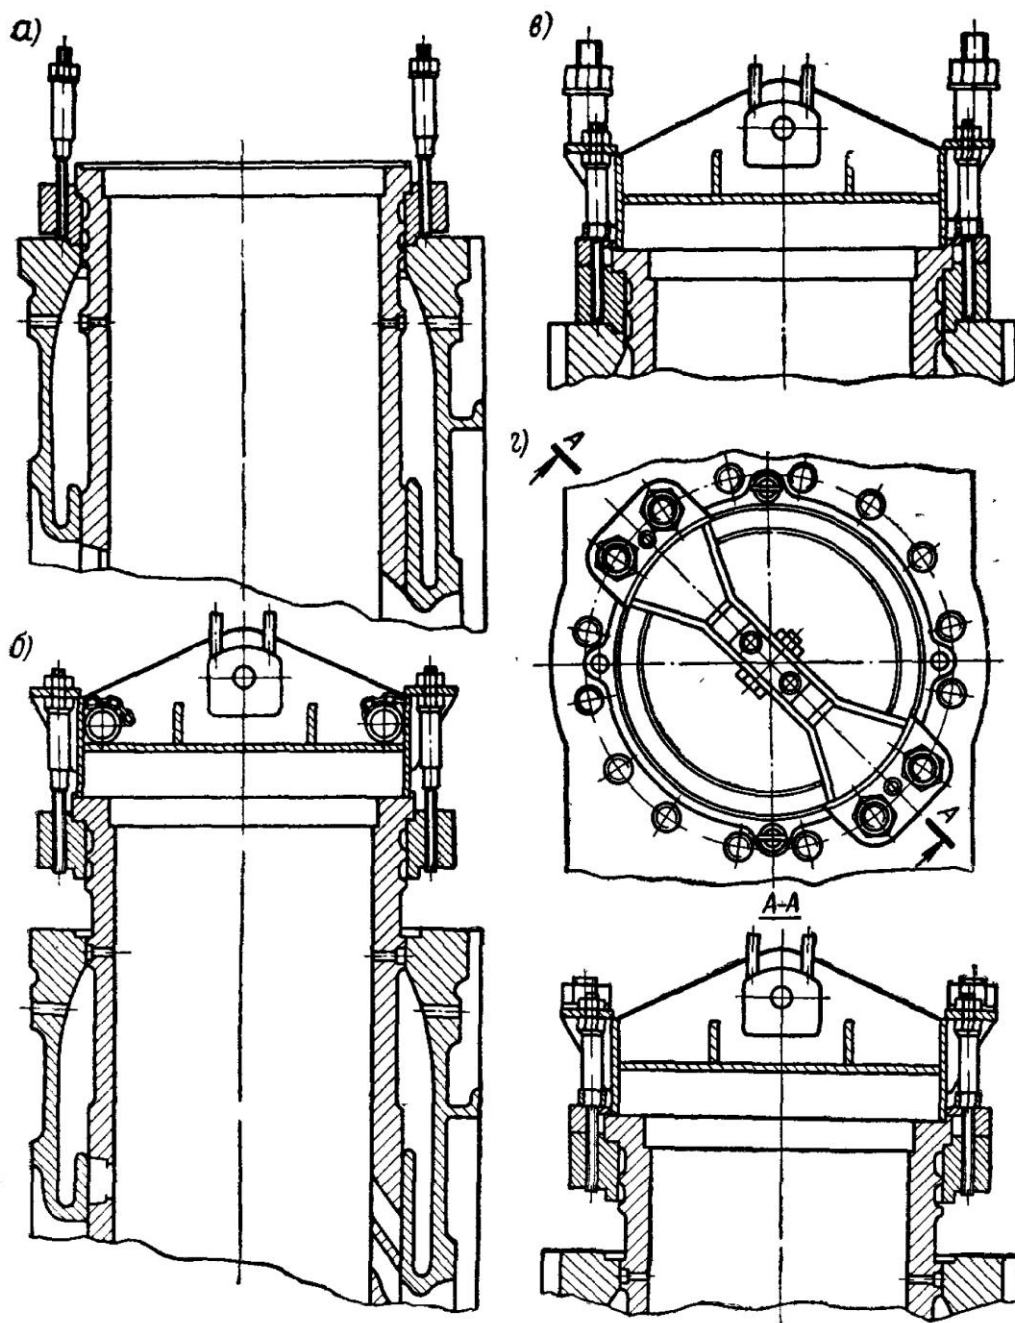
Приспособление фирмы «Зульцер» для выпрессовки и запрессовки цилиндрических втулок
